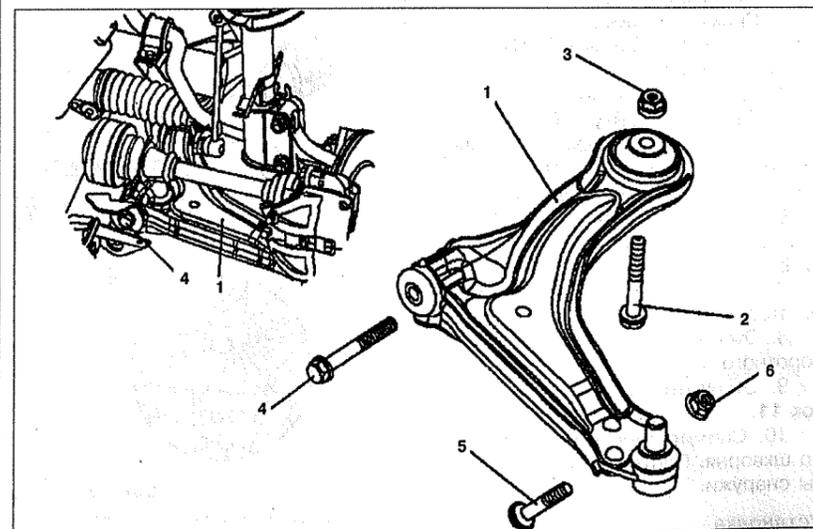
Нижний рычаг подвески (автомобили с двигателями 111.948, 601.970 и 611.980):
